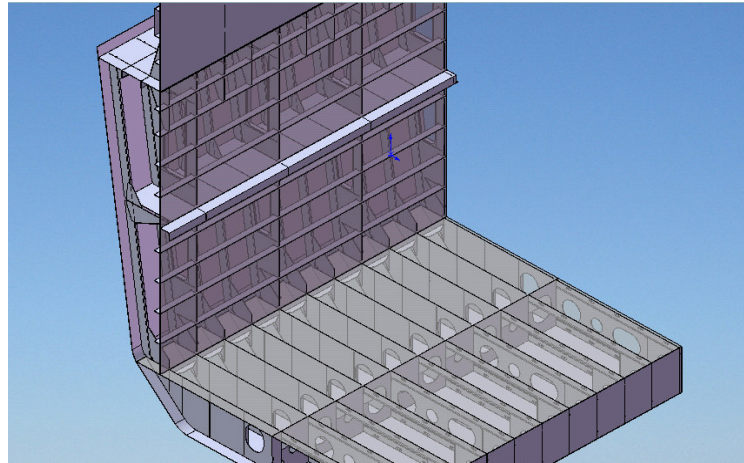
Orta Gövde ile döşekler arasındaki braketler
